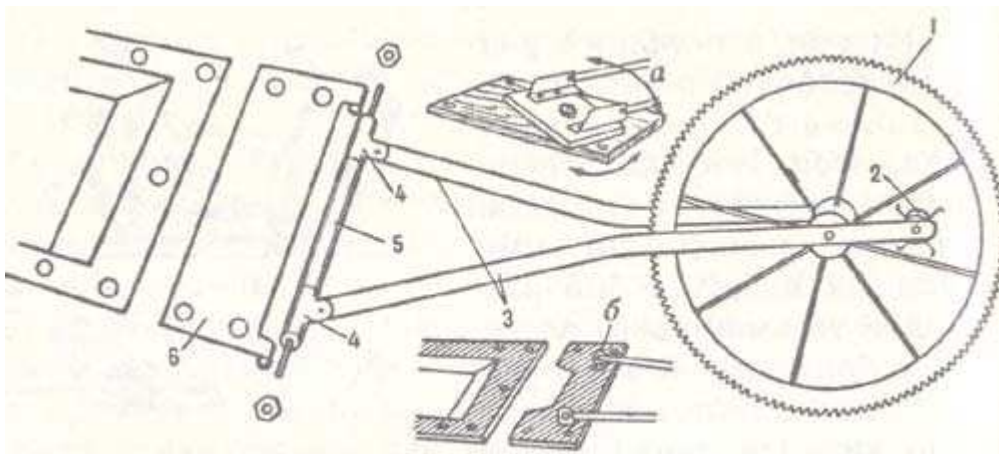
Одометр: 1 — колесо с насечкой; 2 — счетчик оборотов колеса; 3 — тяги; 4 — «косынки» для соединения тяг с осью; 5 — ось; 6 — пластина, а и б — другие способы крепления тяг к санкам (нартам).
